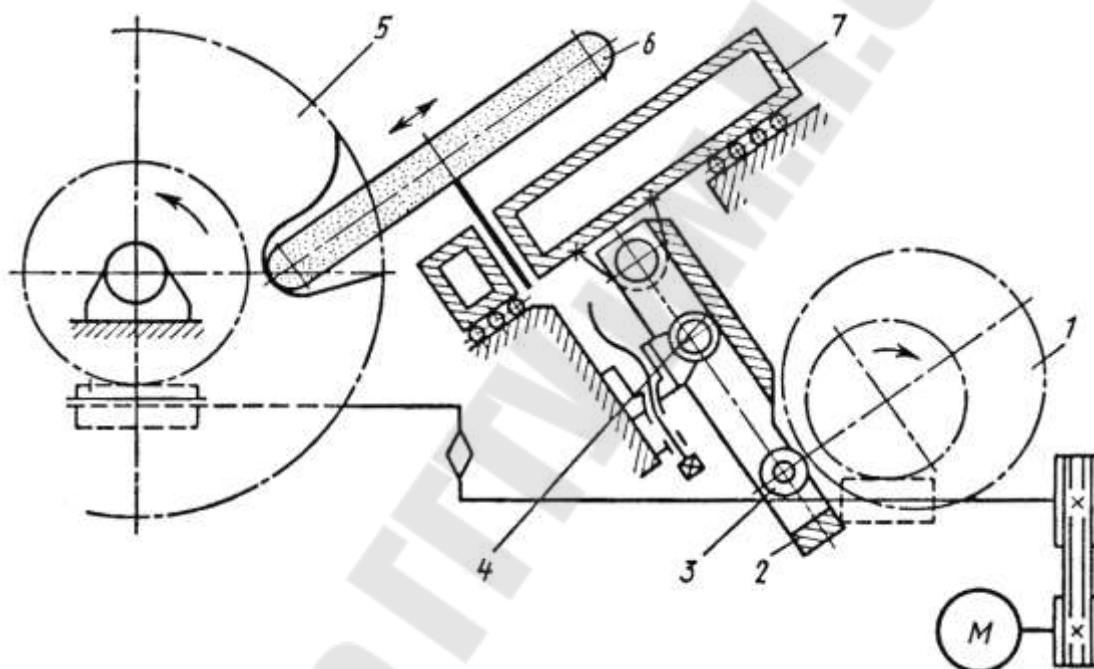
Схема работы полуавтомата модели 3Д692 для заточки дисковых пил: 1 – сменный кулачок; 2 – качающийся рычаг; 3 – ролик рычага; 4 – смещаемый опорный ролик; 5 – затачиваемая пила; 6 – абразивный инструмент; 7 – каретка шлифовальной бабки
